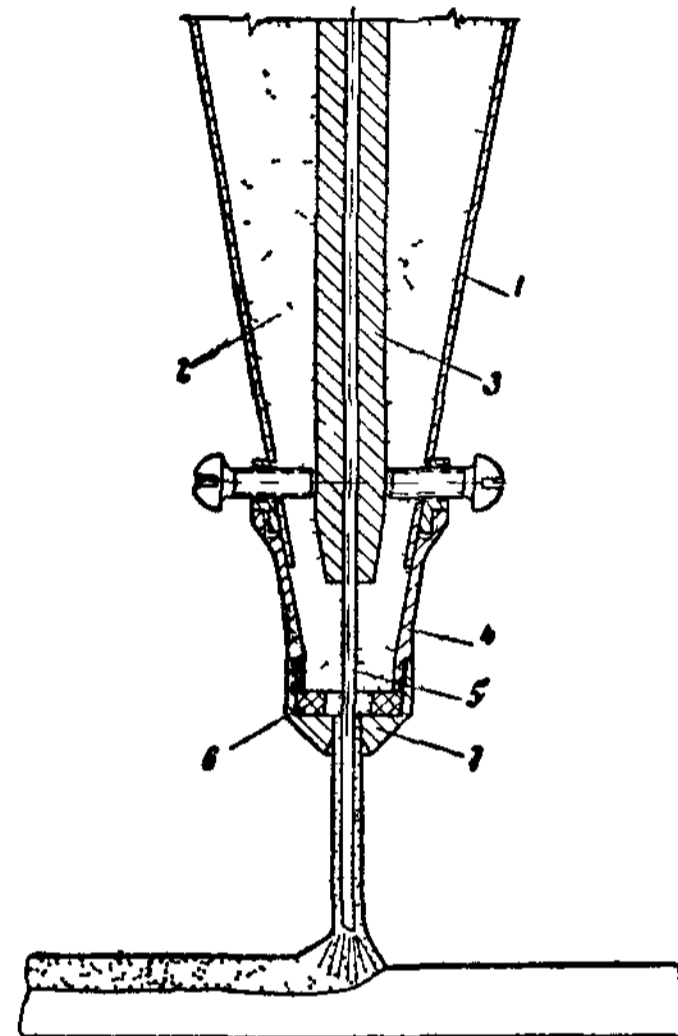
Схема полуавтоматической сварки с намагничивающимся флюсом с применением специального приспособления
